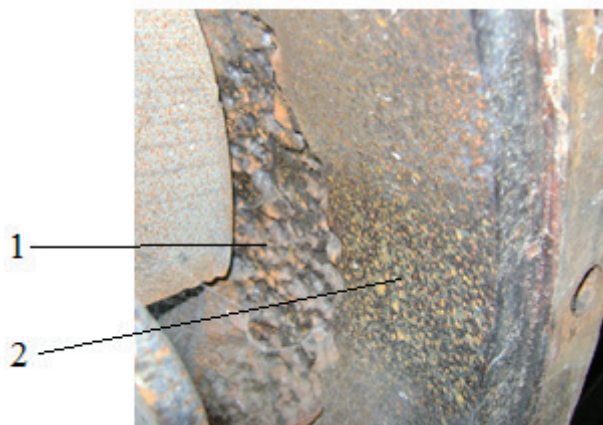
Кавитационный (1) и гидроабразивный износ внутренней поверхности рабочей камеры корпуса водяного насоса (2)
